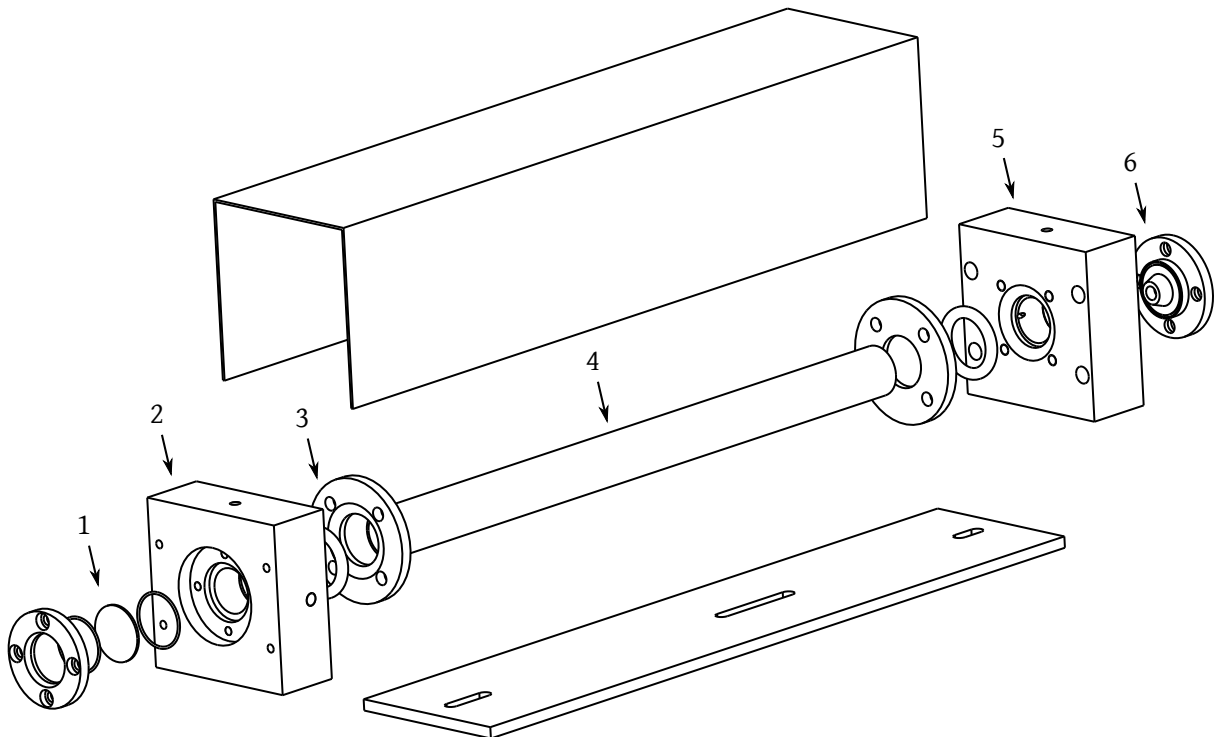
Aerosolbestrahlungskammer, Explosionszeichnung der Baugruppe.
